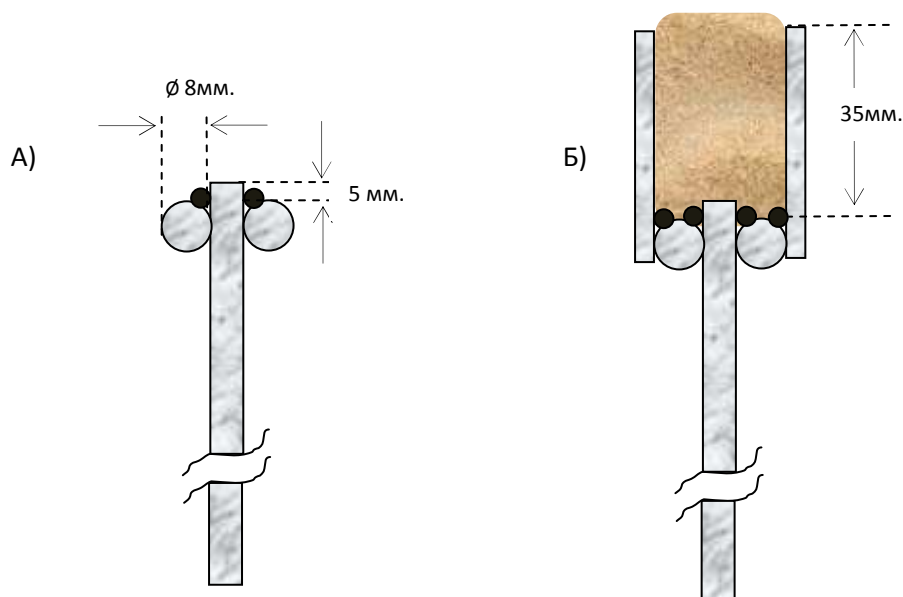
Затворы (черными точками показаны места сварки).
